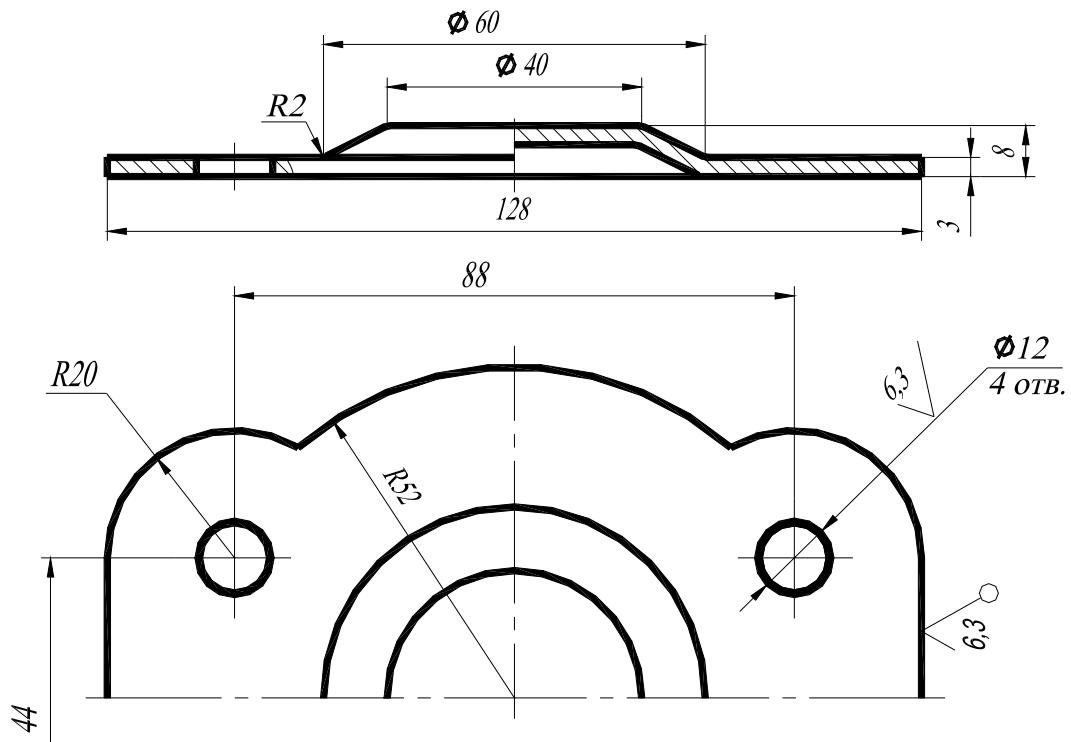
Нанесение размеров детали, изготовленной холодной штамповкой, по матрице
